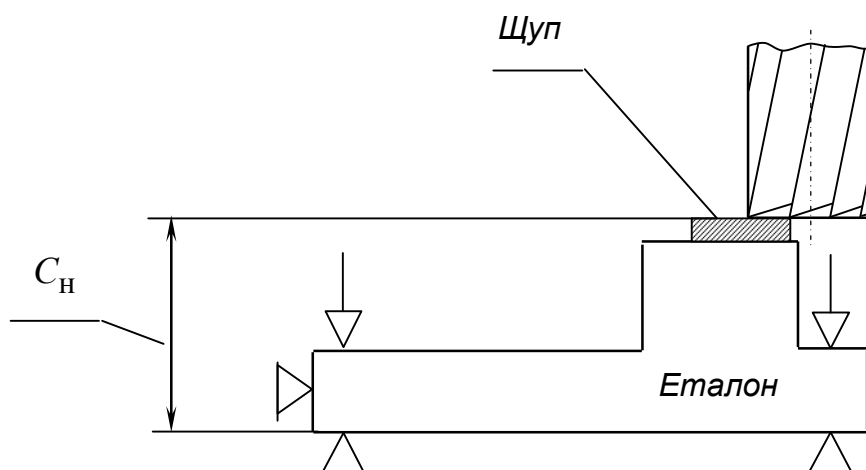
Схема, що пояснює настроювання верстата за еталоном
